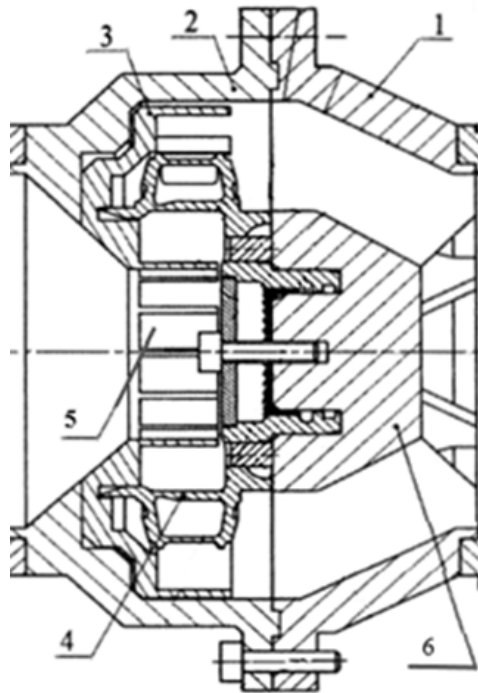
Зоны течения с направляющим аппаратом: 1 – нижняя часть приспособления (направляющая); 2 – верхняя часть приспособления (переходник); 3 – направляющий аппарат; 4 – деталь; 5 – закрытый канал детали; 6 – основа приспособления [114]
